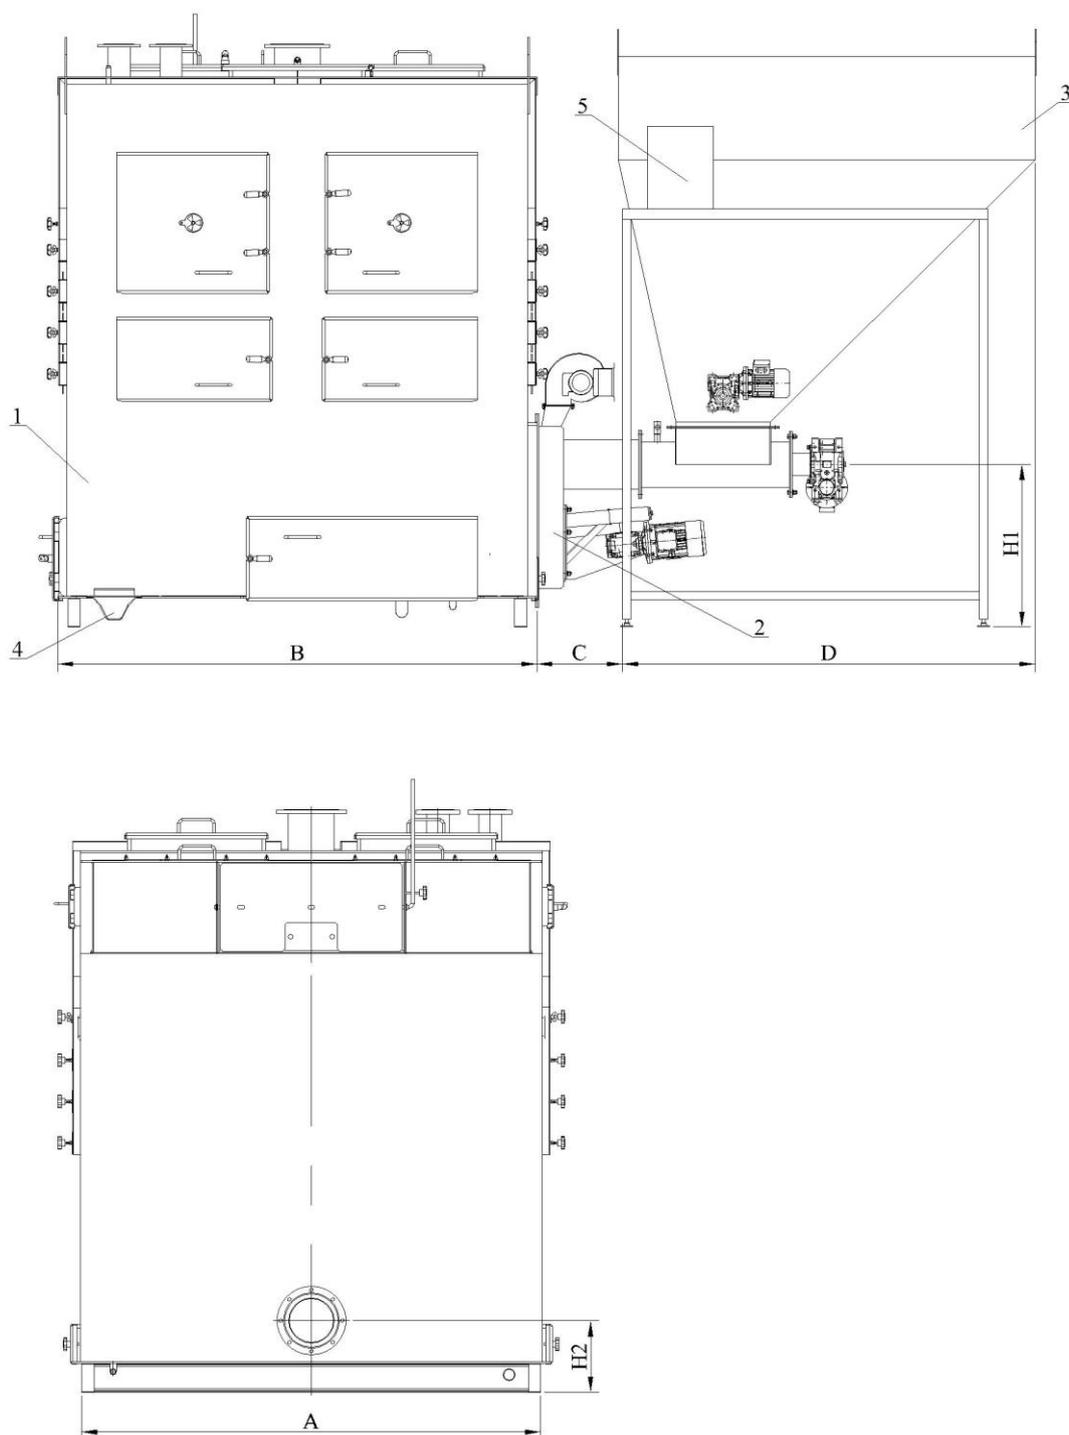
Габаритные и присоединительные размеры котлоагрегата
